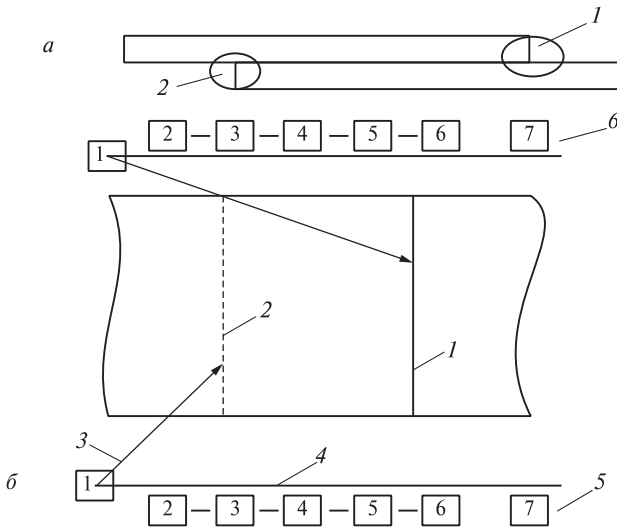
Обозначения сварных швов на чертежах:
